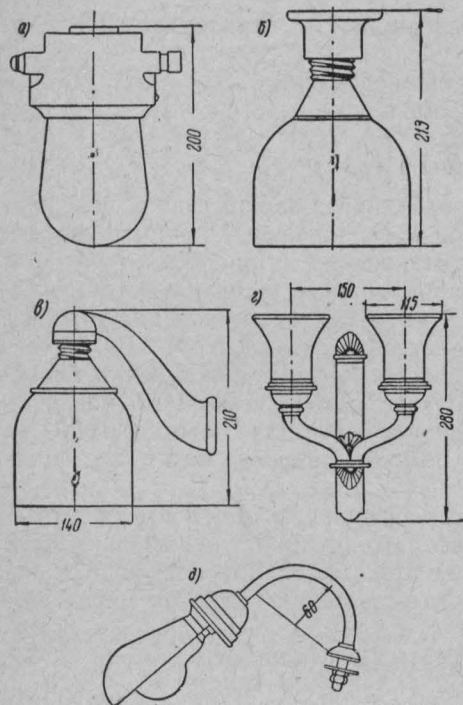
Судовые светильники открытого исполнения: а) подпалубный; б) переборочный; в) настенный; г) двухрожковое бра; д) щитковое бра
